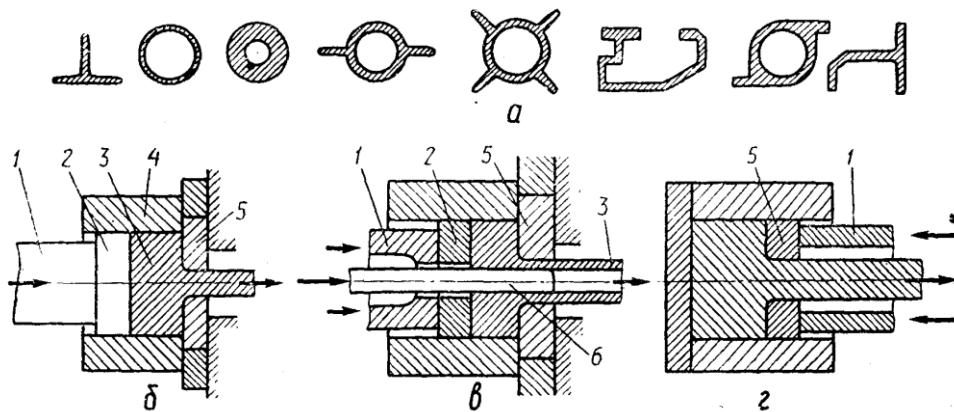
Примеры прессованных изделий и схемы прессования
